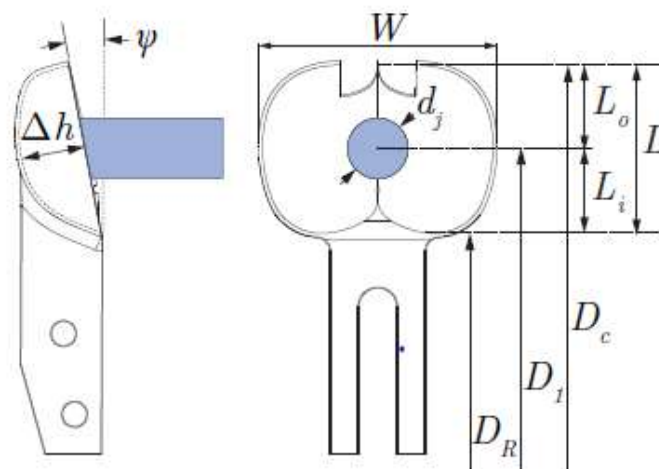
Dimensiones de un cucharón de una Turbina Pelton
